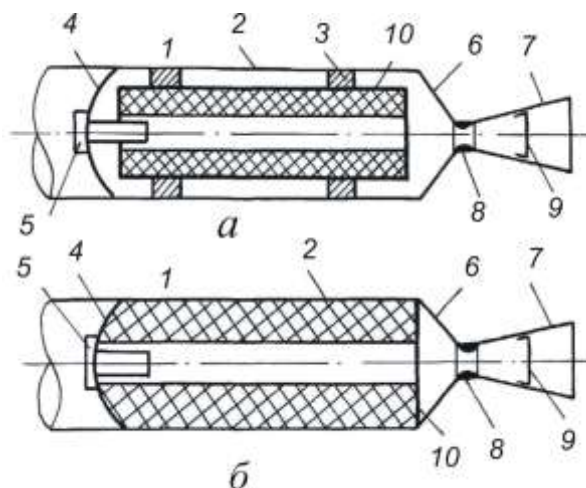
Схеми двигунних установок на твердому паливні:
